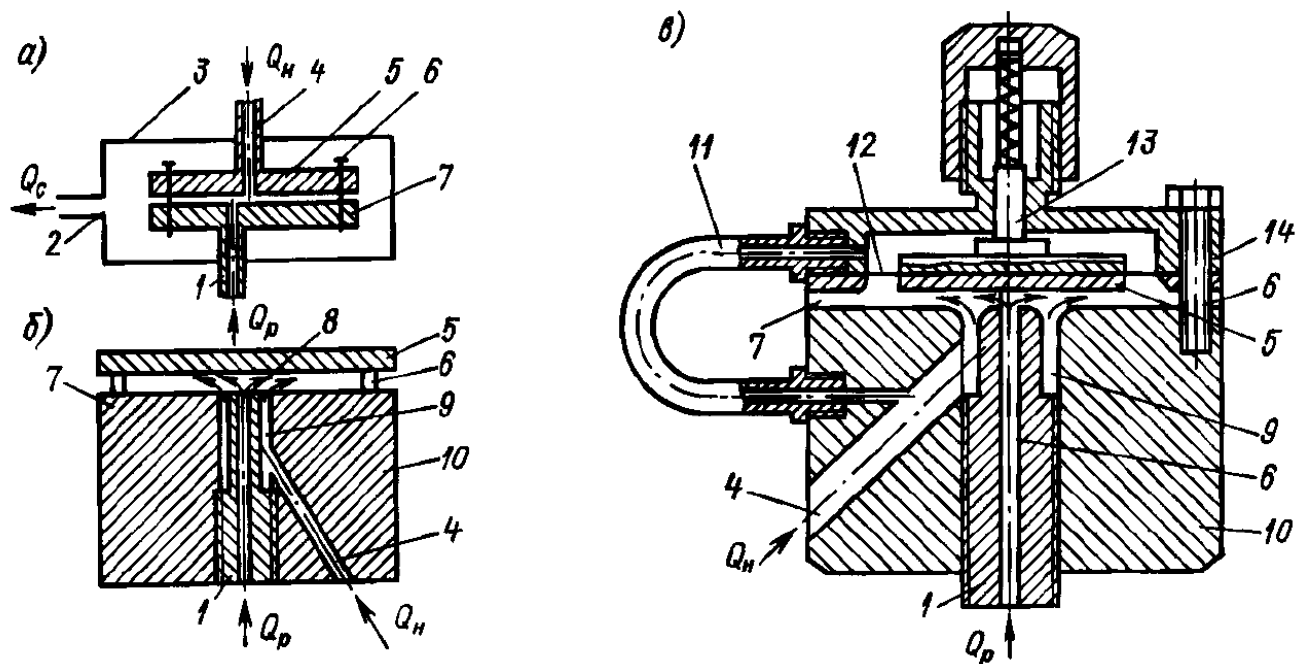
Схеми щілинних струменевих насосів [9]: *а* - а. с. 210663; *б* - а. с. 338687; *в* - а. с. 901654; 1 – трубка; 2 – патрубок; 3 – кожух; 4 – всмоктувальний патрубок; 5 – пластина; 6 – кріплення; 7 – пластина; 8 – сопло; 9 – проточки; 10 – корпус; 11 - трубка; 12 – діафрагма; 13 – шток; 14 – фланець.
